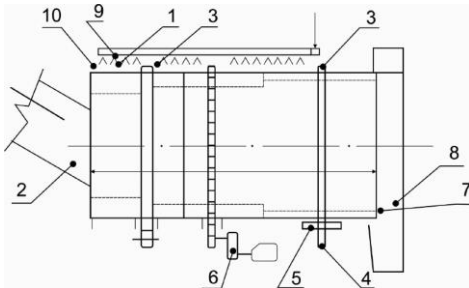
Схема барабана-стабілізатора: 1- барабан; 2- завантажувальна лійка; 3- бандажі; 4- опорні ролики; 5- упорні ролики; 6- привід; 7- полиці; 8- розвантажувальна камера; 9- форсунки для зрошення пристрою водою; 10- кільцеві ребра.
